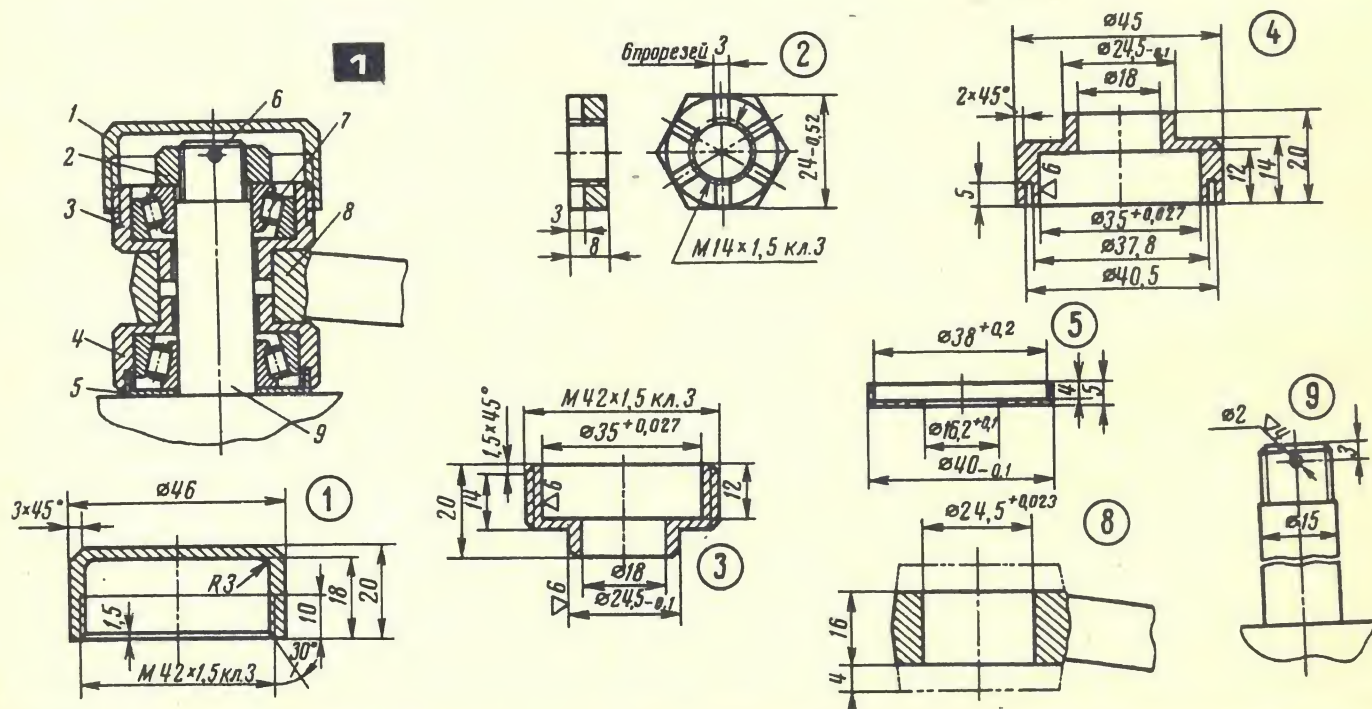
1 — крышка; 2 — гайка; 3 — верхняя обойма; 4 — нижняя обойма; 5 — чашка; 6 — шплинт; 7 — подшипник; 8 — головка маятникового рычага; 9 — ось рычага.
